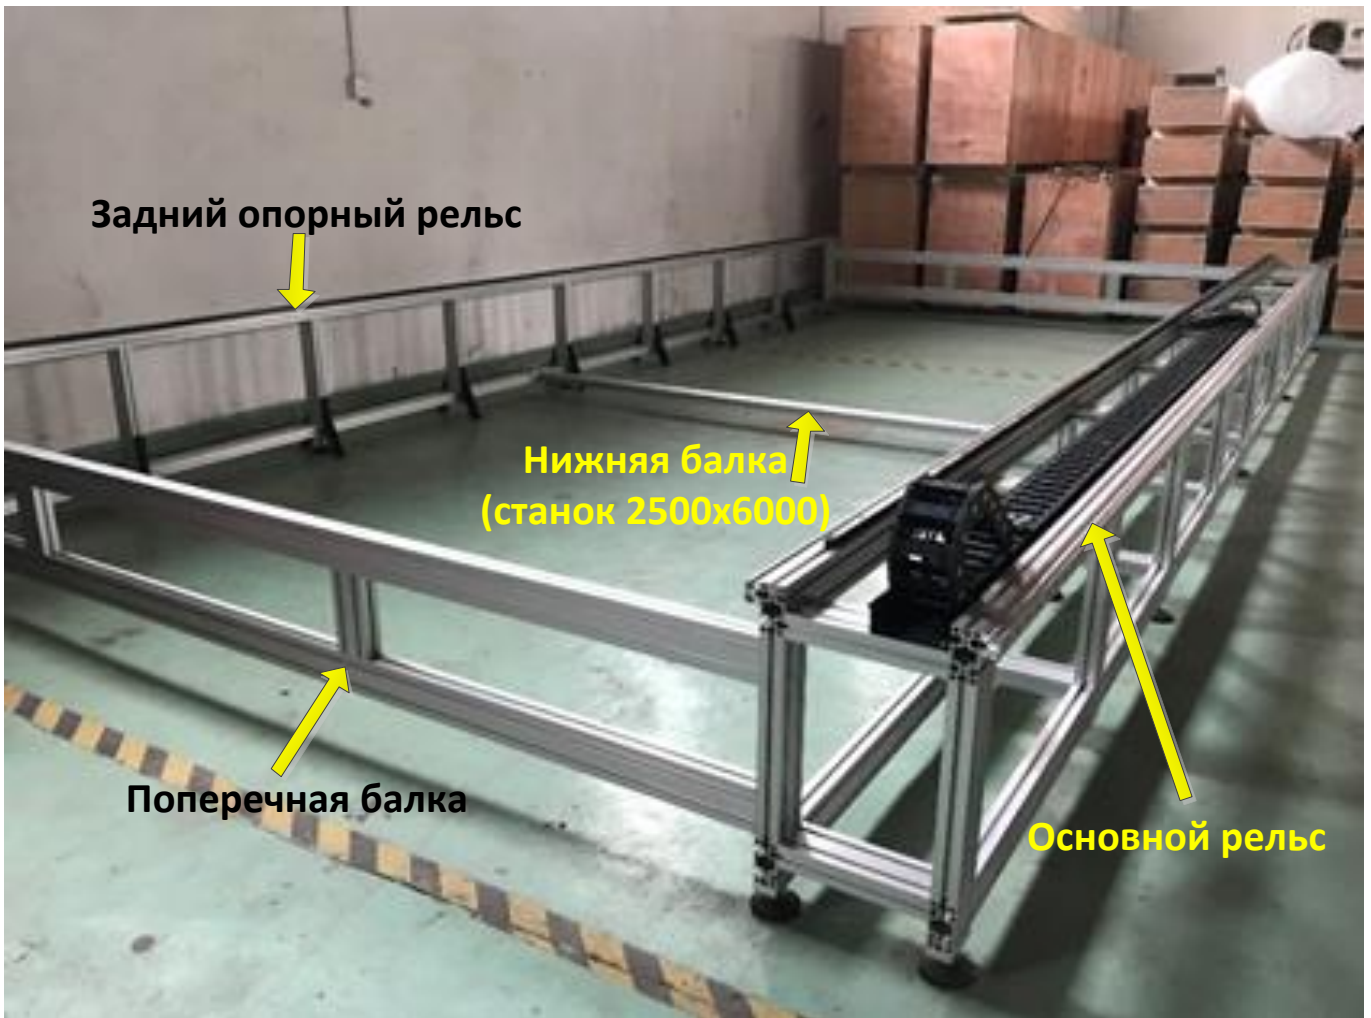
Корпус станка. Вариант 6-ти метрового станка (2500x6000).
